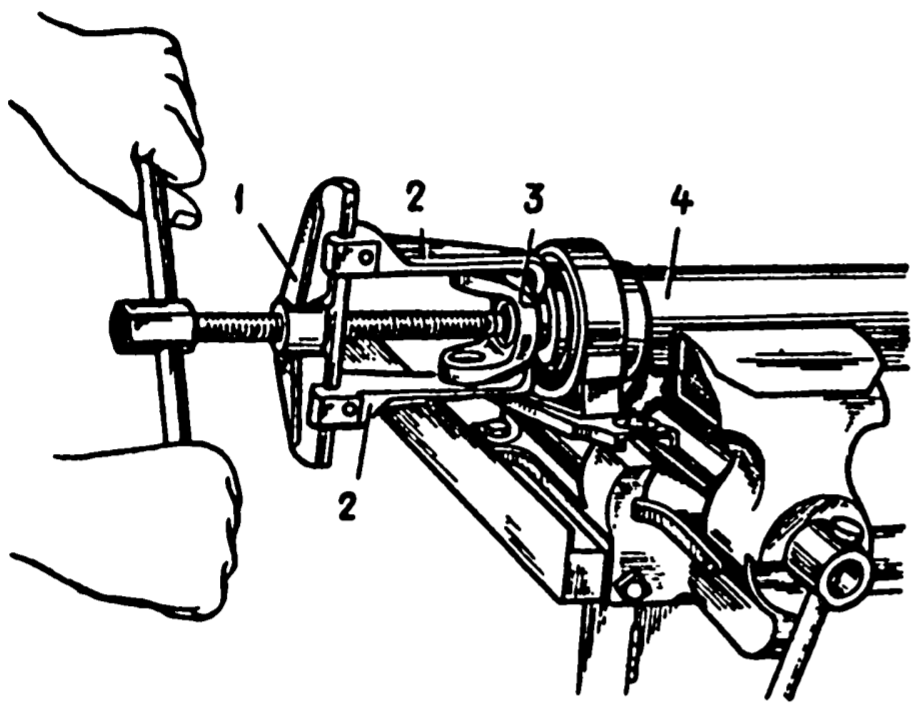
Снятие вилки с переднего карданного вала: 1 - съемник А.40005/1/5; 2 - рычаги съемника; 3 - вилка переднего карданного вала; 4 - передний карданный вал
